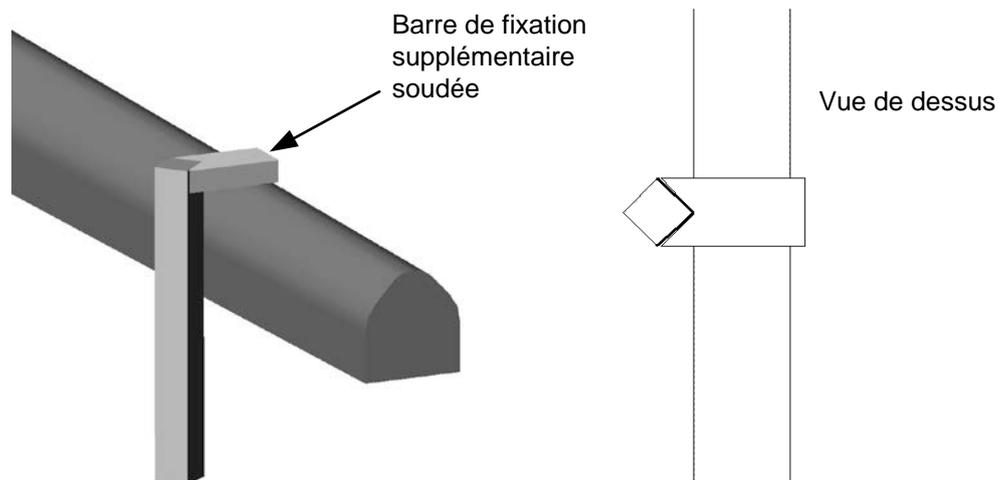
Barre de montage carrée soudée au bras de la pale décapeuse
